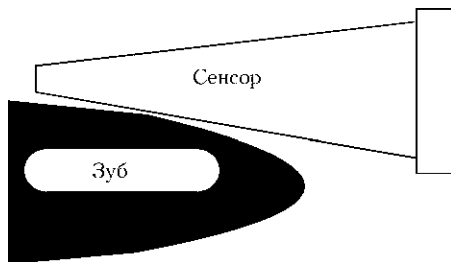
Контакт сенсора с зубом зубчатой передачи
